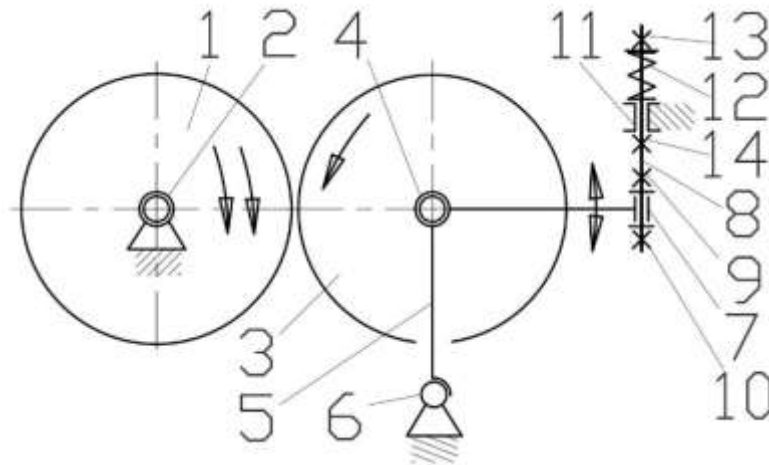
Схема двухвалкової дробарки.
